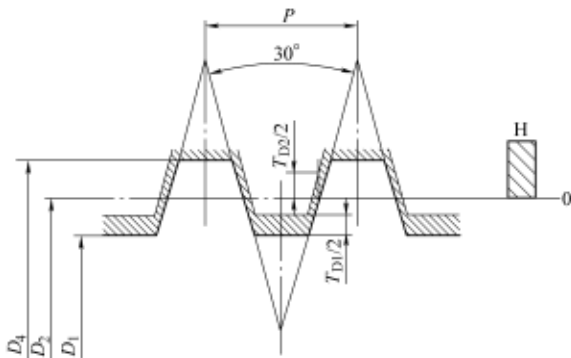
梯形螺纹内螺纹的公差带位置
